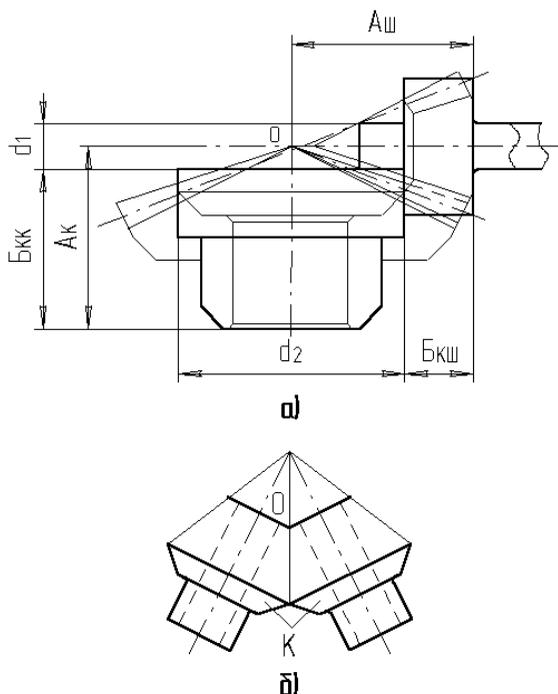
Схемы сборочных калибров для конических зубчатых передач
